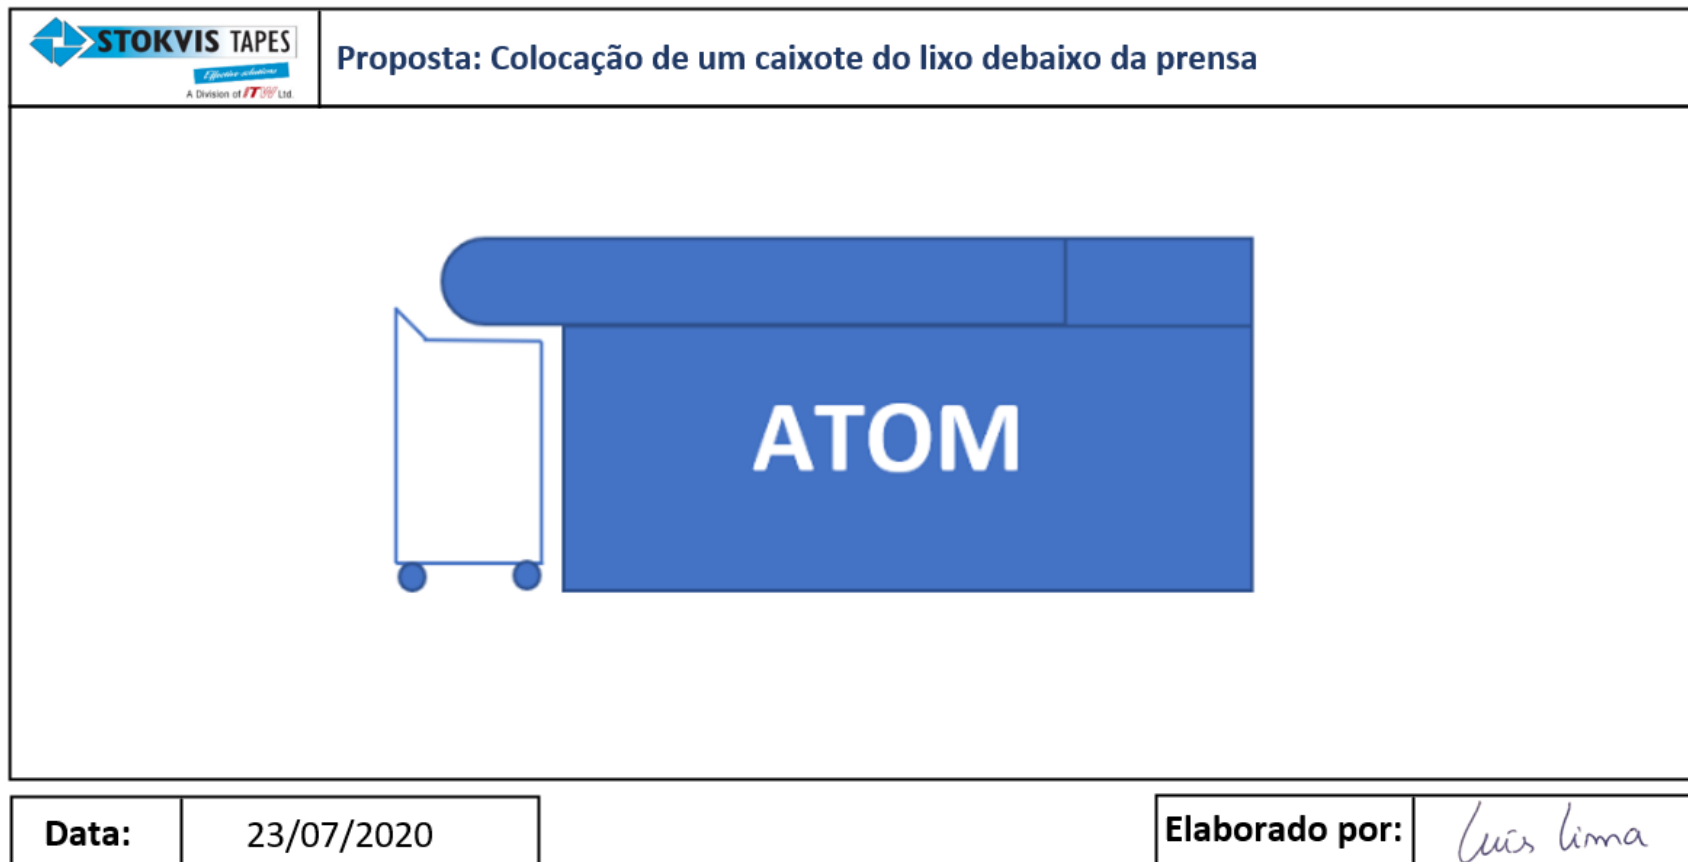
Esquematização da proposta para colocação de um caixote do lixo debaixo da prensa
